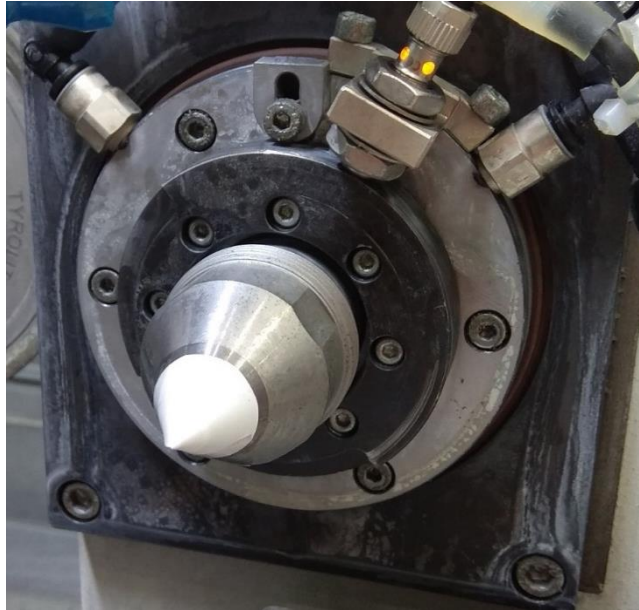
Papel revelador de presión colocado sobre la superficie del punto.
